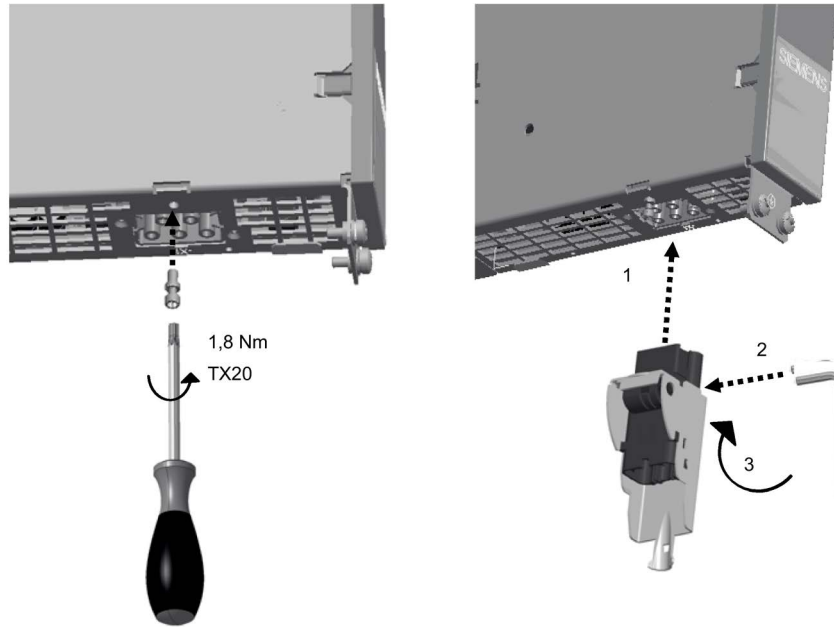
Montaje tomando como ejemplo un conector engastable
